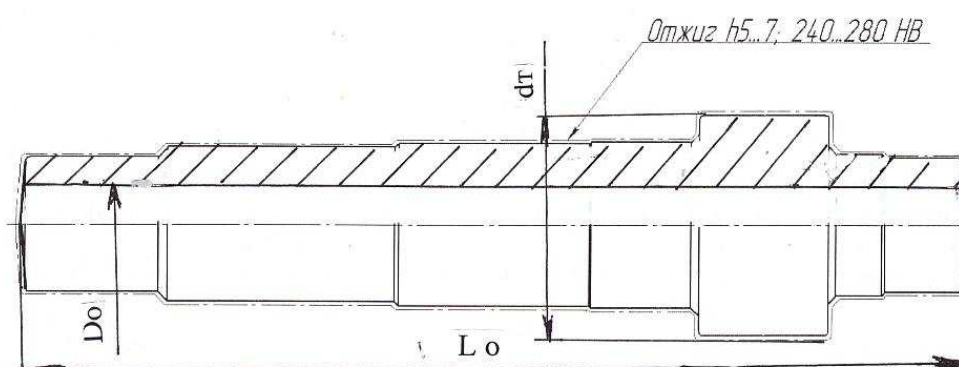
Эскиз штампованной из трубы 123x6,5x610 (ММ) ГKM заготовки пустотелого вала
